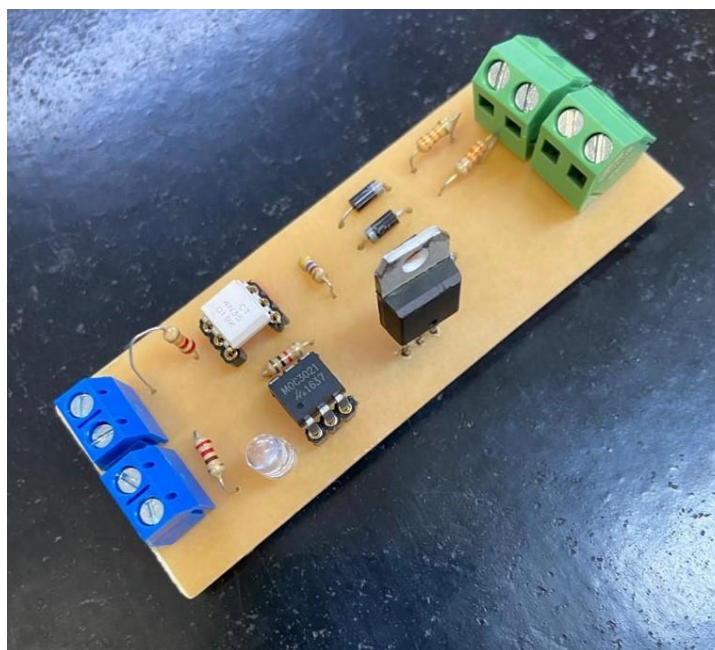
Componentes soldados na placa de circuito impresso
